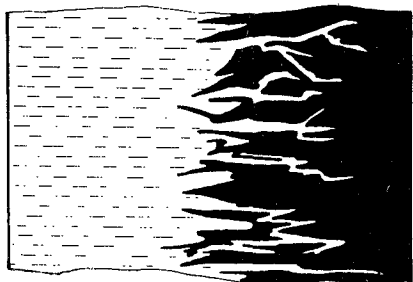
Схема капиллярных каналов в двухфазной области затвердевающей отливки
